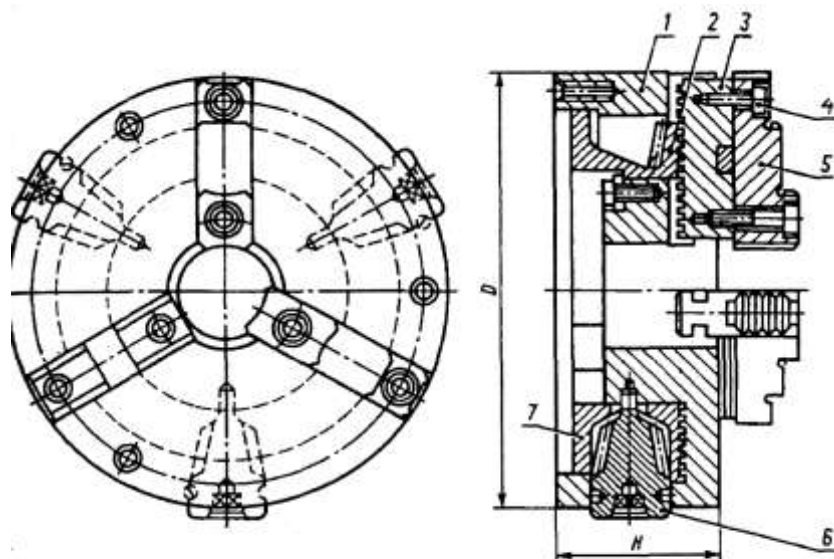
Трехкулачковый спирально-реечный самоцентрирующий патрон
